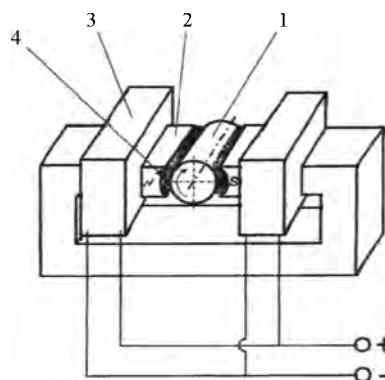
Схема магнитно-абразивной обработки поверхностей тел вращения: 1 – обрабатываемая заготовка; 2 – полюсный наконечник; 3 – электромагнитная катушка; 4 – порошок
